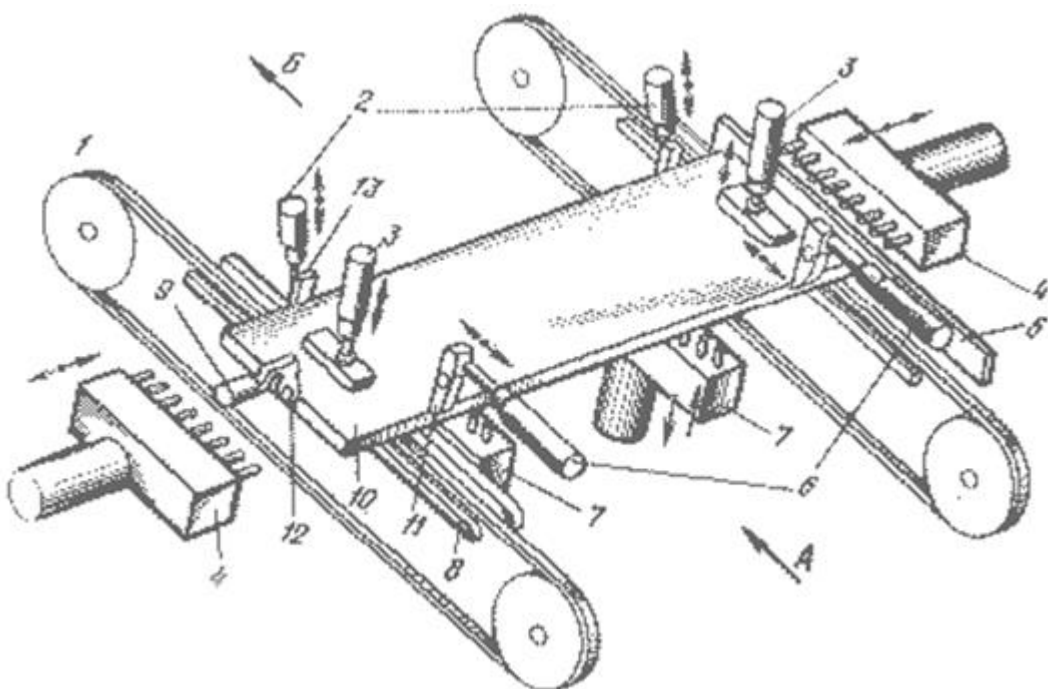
Свердлильно-присадний верстат прохідного типу.
